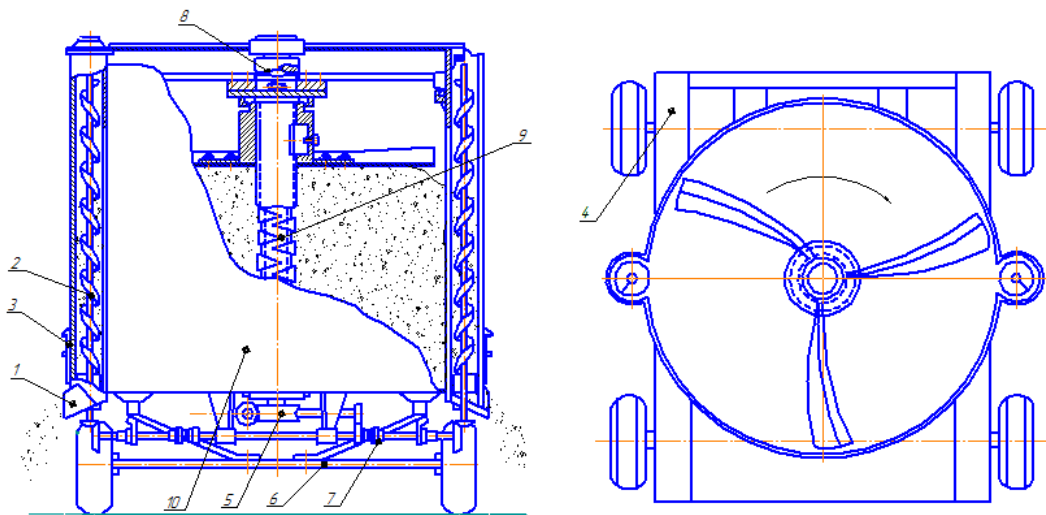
Кормороздавач: 1 – направляючий лоток; 2 – шнек; 3 – шибер; 4 – рама; 5 – приводна станція; 6 – опора; 7 – муфта; 8 – кришка; 9 – вал; 10 – корпус.
